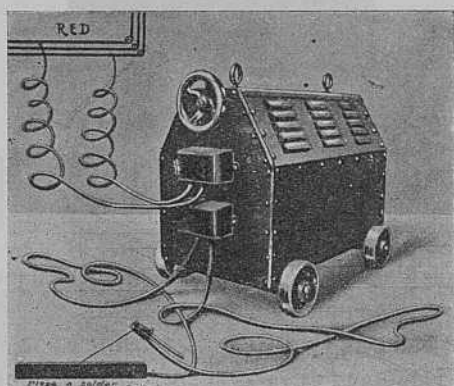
Transformador para soldadura eléctrica.
